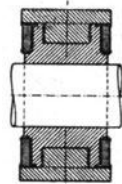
Feldmagnet mit aufgeschraubten Polen.
